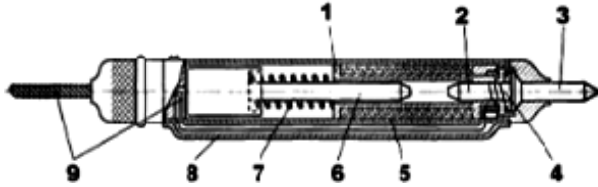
Електричний кернер: 1 – втулка; 2 – стрижень; 3 – кернер; 4, 7 – прижини; 5 – котушка; 6 – ударник; 8 – корпус; 9 – електричний провід
